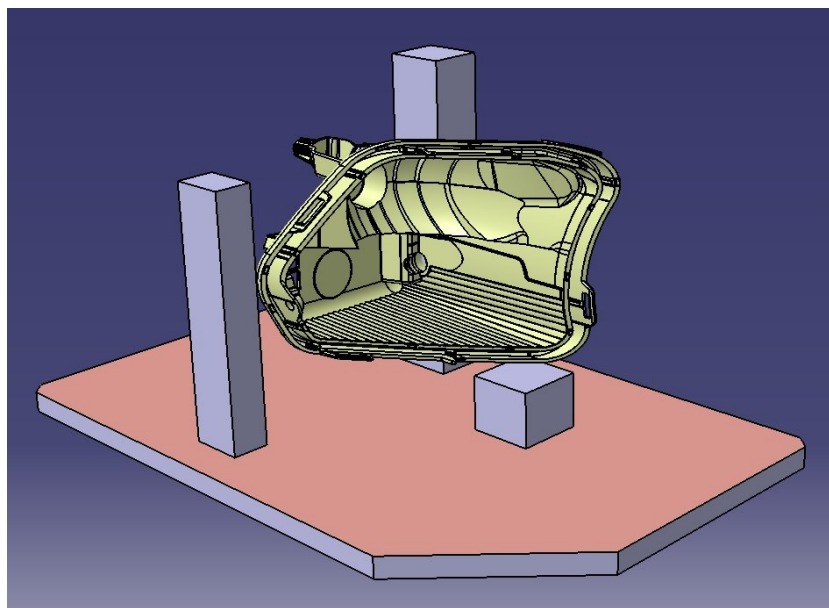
Tvorba vztažného, souřadného systému přípravku
